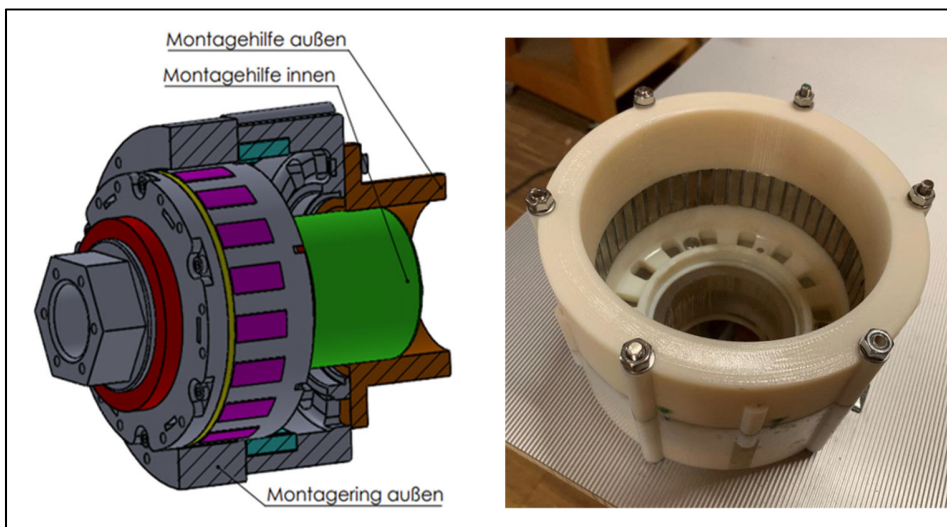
Schnittansicht CAD-Modell mit Montagerrichtungen des Außenrings links, und bei der Montage rechts [8]
